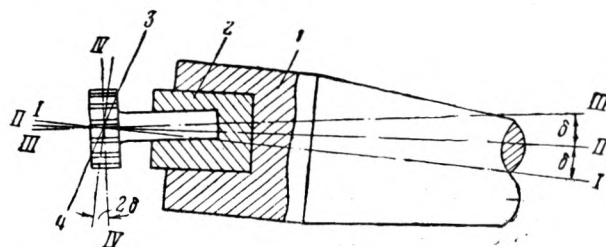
Схема регулирующего патрона для фрезерования пазов под сегментные шпонки типа Вудруфа. 1 — корпус патрона; 2 — втулка, закрепленная под углом δ к оси вращения 1-1; 3 — фрезер, заложенный под углом δ к оси втулки II-II
